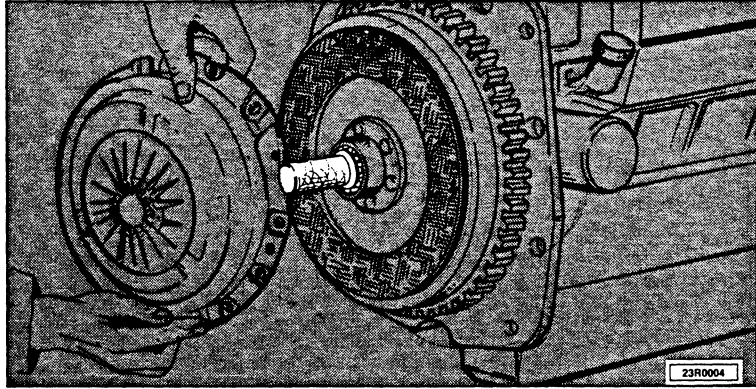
Montaje del grupo embrague mediante la herramienta 5.9030.256.4/10.
